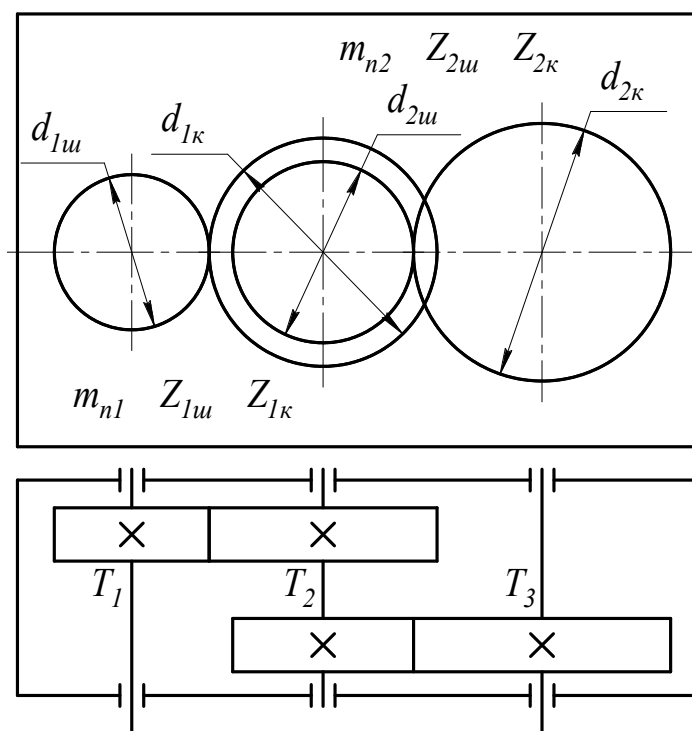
Кинематическая схема и условные обозначения двухступенчатого цилиндрического редуктора
